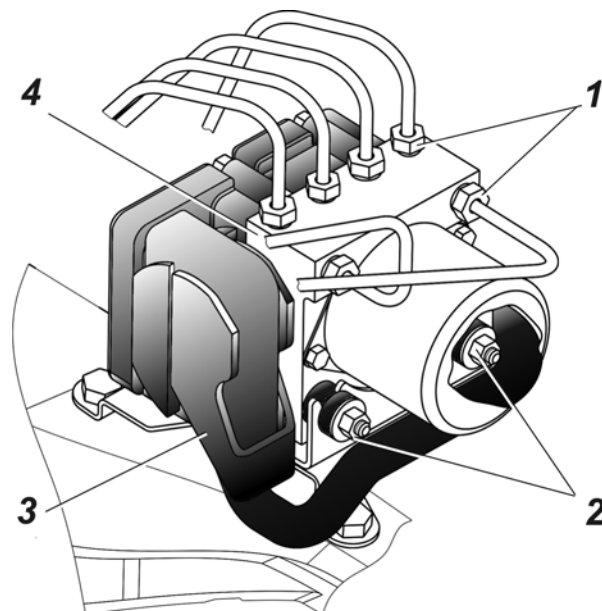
Снятие гидроагрегата АБС: 1 - гайки трубопроводов; 2 - гайки крепления гидроагрегата к кронштейну; 3 - колодка проводов жгута АБС; 4 - гидроагрегат АБС
